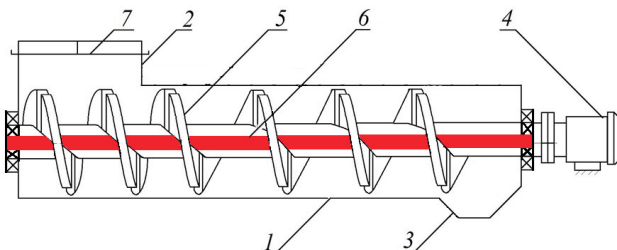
Установка для приготовления почвенного грунта непрерывного типа
